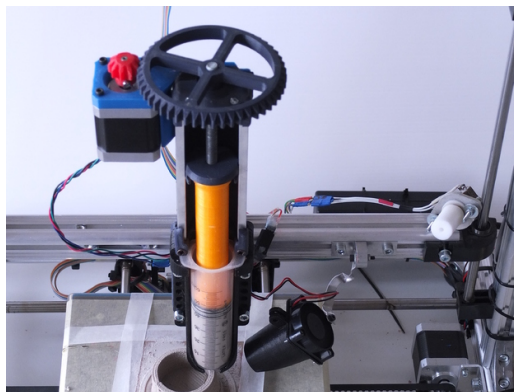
Representació impressora 3D per Syringe Extrusion [56].
